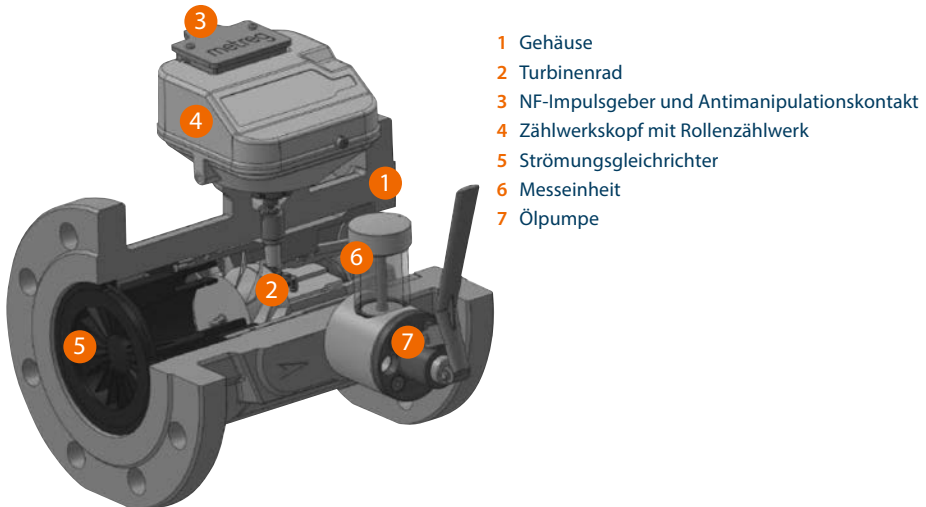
Schnittbild des MTM Turbinenradgaszählers
